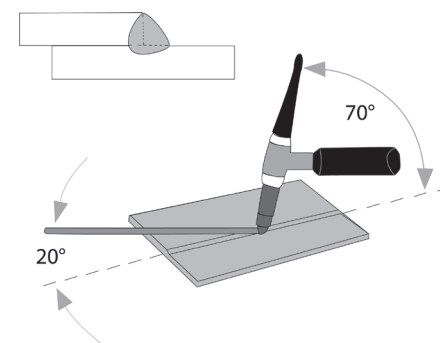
Положення «TIG»-пальника під час виконання зварювання з'єднання внапусток.
